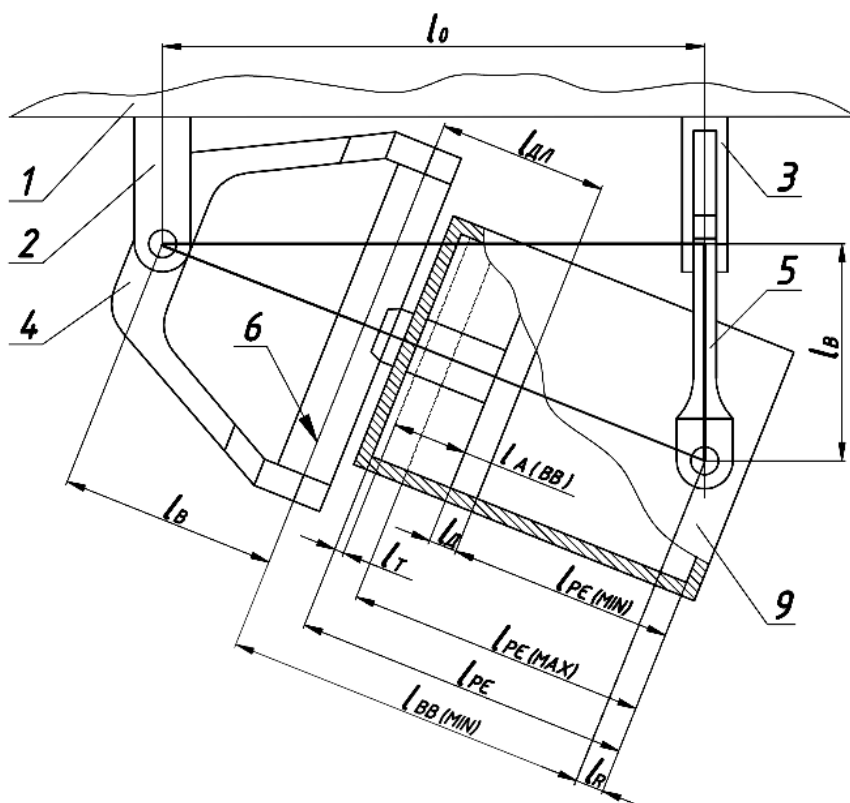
Розроблена машина для обробки деталей – вид зверху
